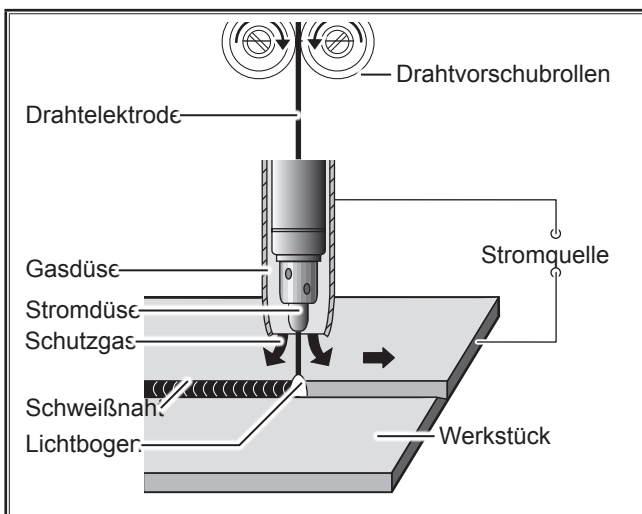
MIG/MAG-Schweißverfahrens
